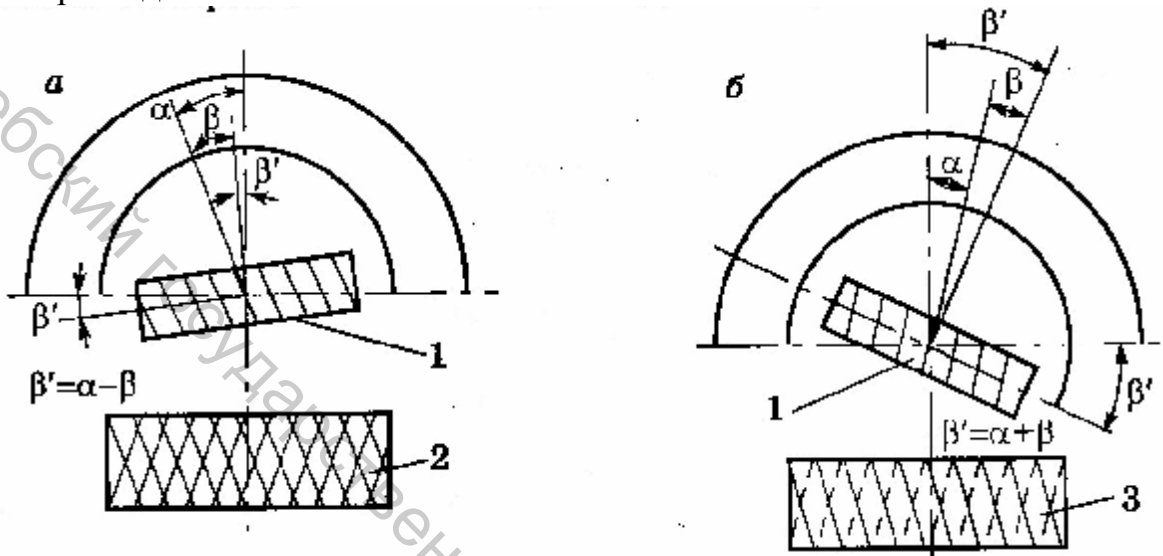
Установка червячной фрезы при зубонарезании цилиндрических зубчатых колес с косым зубом: 1 — правозаходная фреза; 2 — заготовка правозаходного зубчатого колеса; 3 — заготовка левозаходного зубчатого колеса
